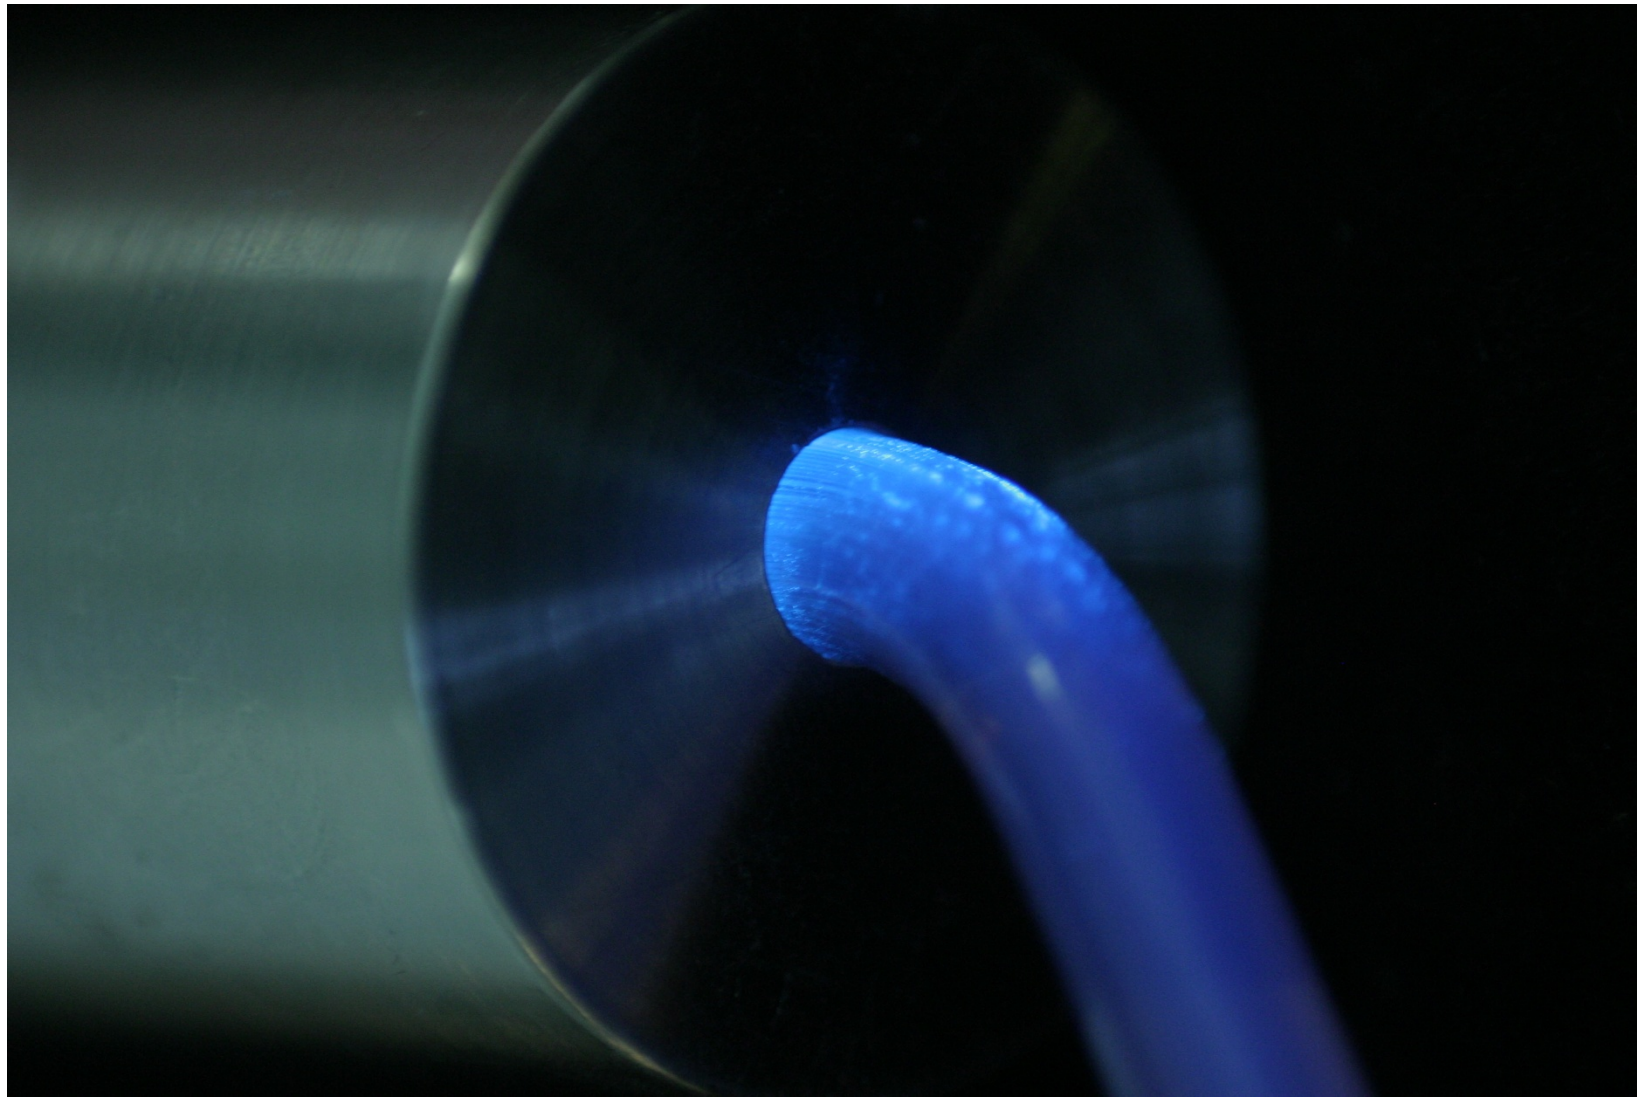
Conjunto após a colocação do cilindro externo (d) e a ponta do aparelho fotopolimerizador.
